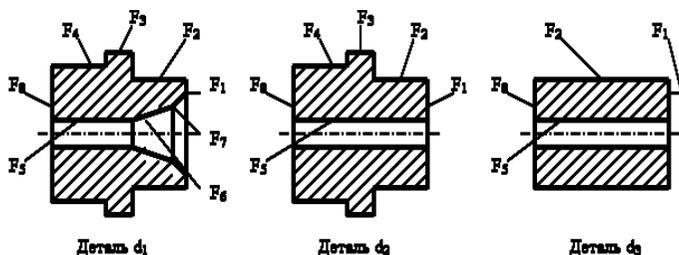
Эскизы заготовок при их токарной обработке
